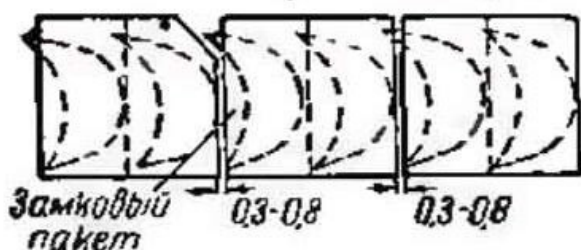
Вид сверху на бандажи сварных пакетов рабочих лопаток с замковым пакетом
